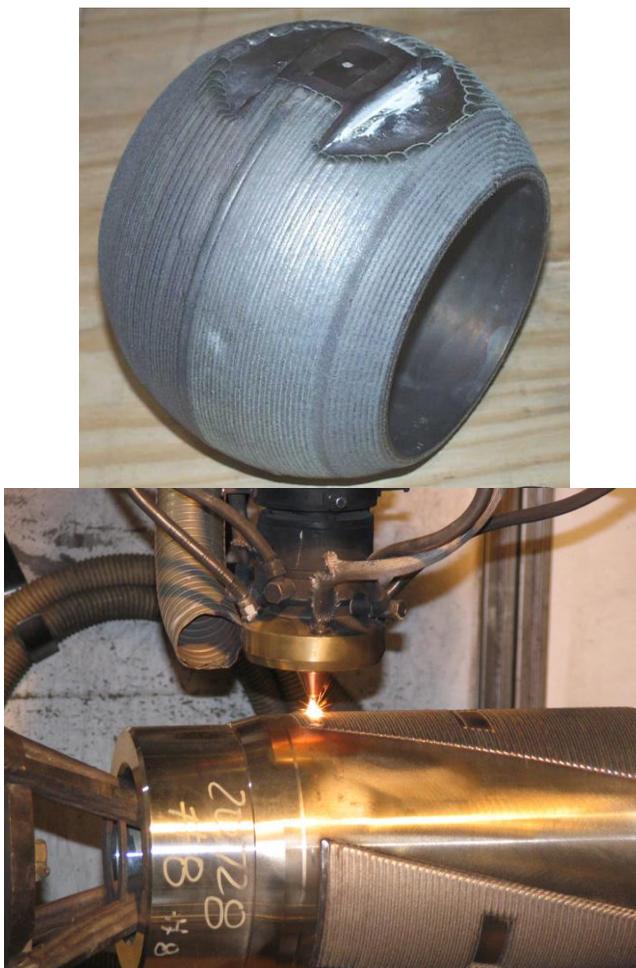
Выборочная наплавка поверхности шарового крана и перепускного клапана.
